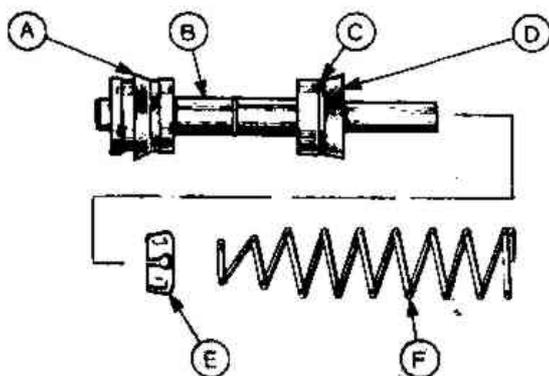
Вторичный поршень в сборе (Разд.15)
